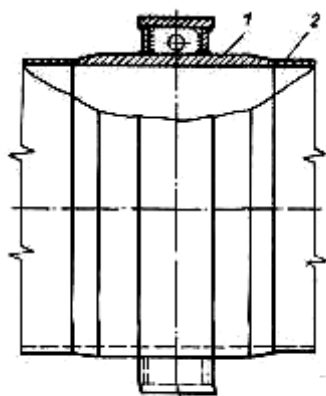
Сварно-прокатный бандаж; разрезный в корпус печи
